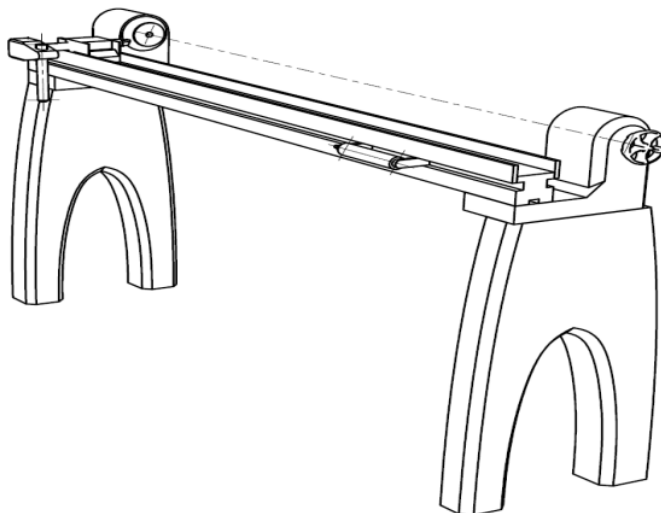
Копіювально-фрезерний верстат JET, [4]
